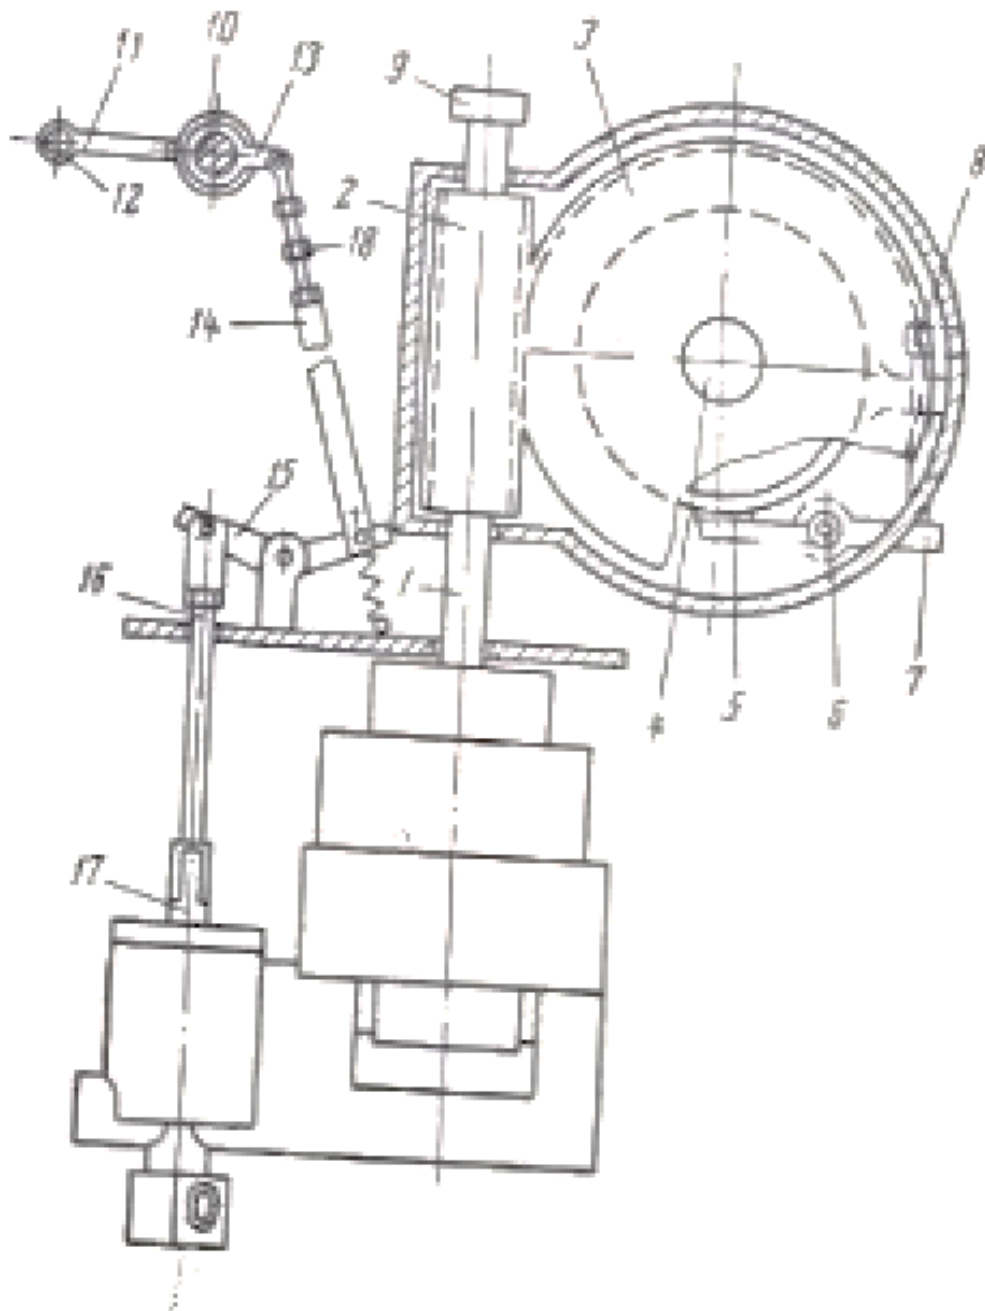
Редуктор для обертання навою та скалковий механізм
